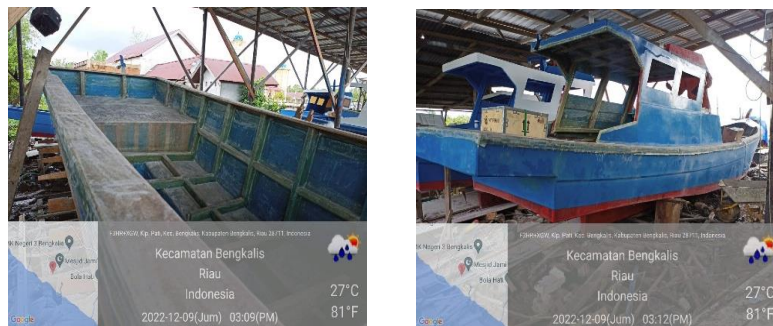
Pemasangan bangunan atas 2 GT dan Pemasangan gading 3 GT
